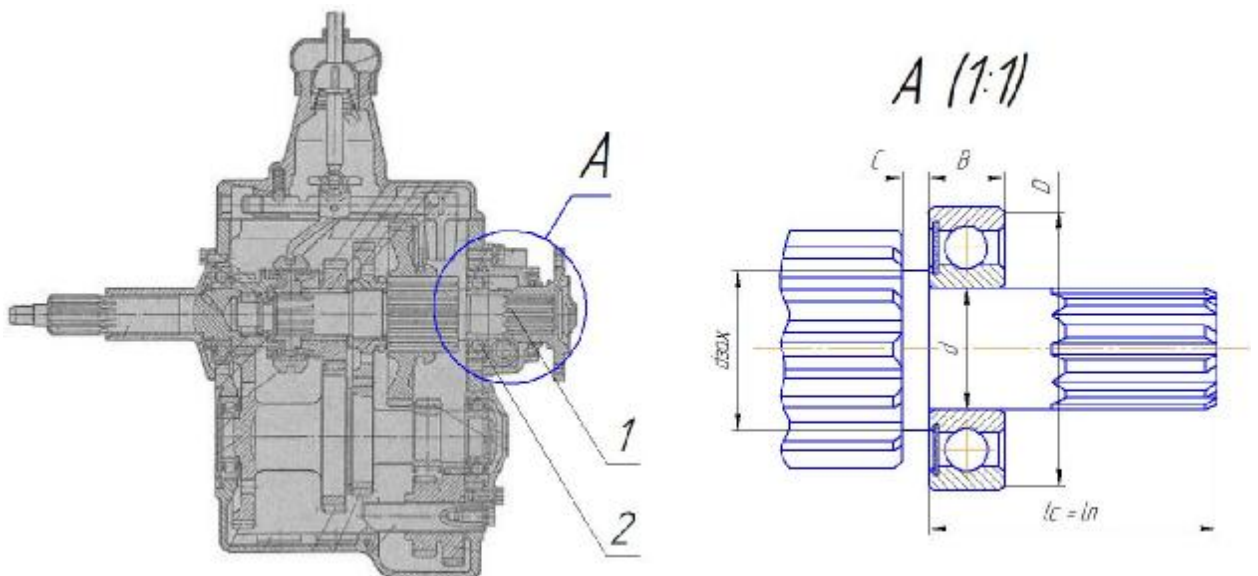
Схема встановлення кулькового підшипника на вторинному валу коробки передач автомобіля ГАЗ-3307: 1 – вторинний вал; 2,3 – шестерня першої передачі; 4 – проміжний вал; 5 – первинний вал; 6 – синхронізатор; 7 – підшипник вторинного вала.
